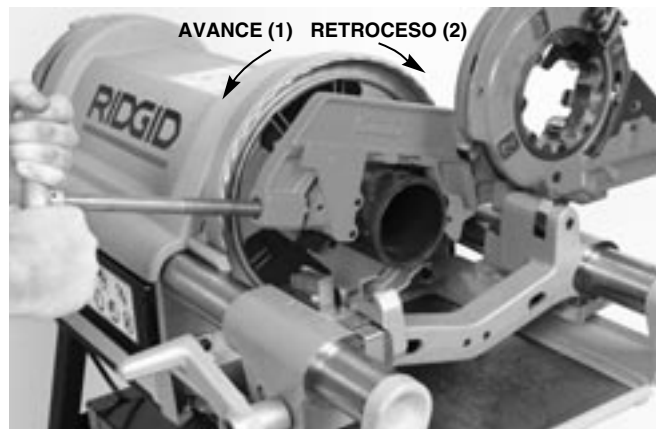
Corte de un tubo con el cortador 764: rotación de la máquina
